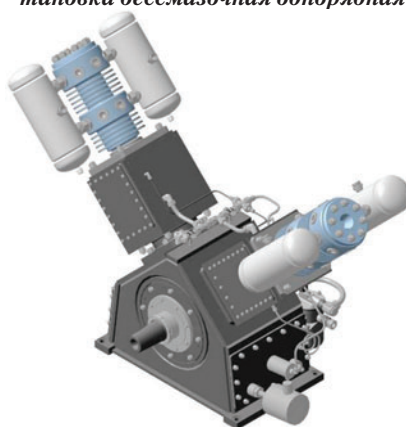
Дожимная компрессорная установка бессмазочная двухрядная
